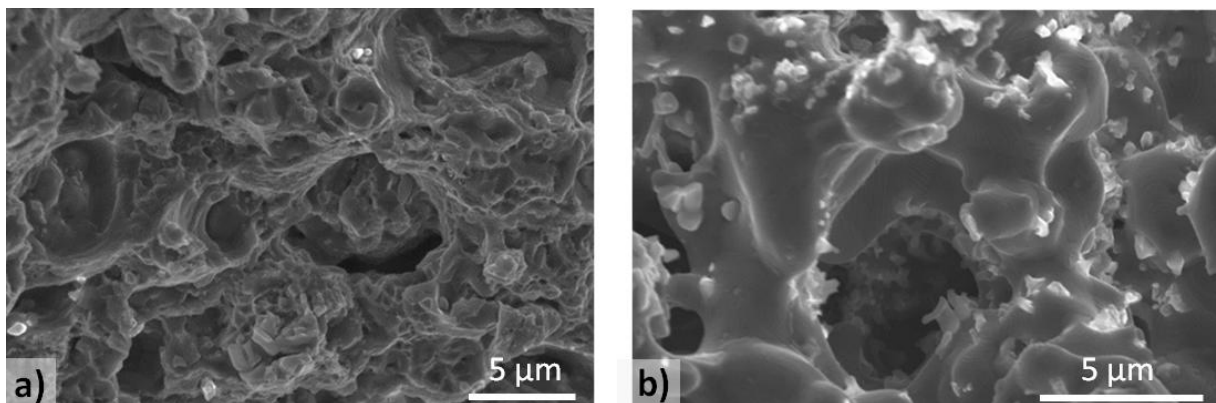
Grandissement des faciès de rupture des éprouvettes de type Z.R. : a) 700°C, b) 950°C
